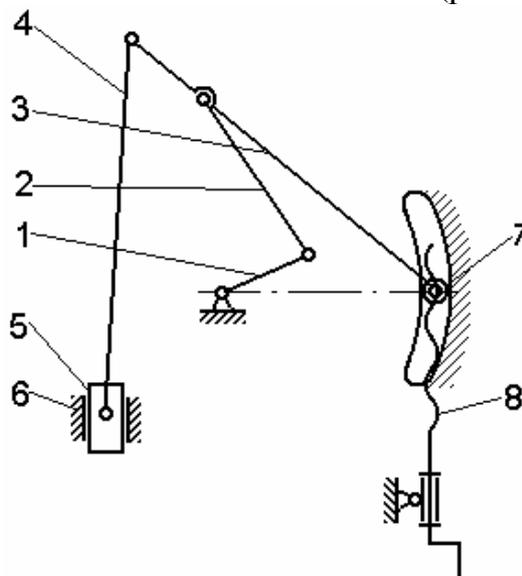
Кинематическая схема шестизвенного ударного механизма с регулируемым положением опоры коромысла
